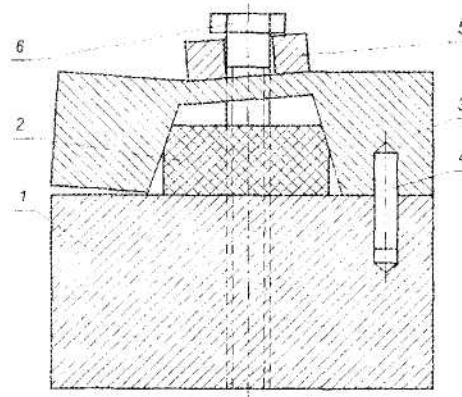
Різець з механічним кріпленням різальної пластини для обробки напилених покриттів (вид зверху, розріз): 1 – державка; 2 – різальна пластина; 3 – сепаратор; 4 – штифт; 5 – прихват
